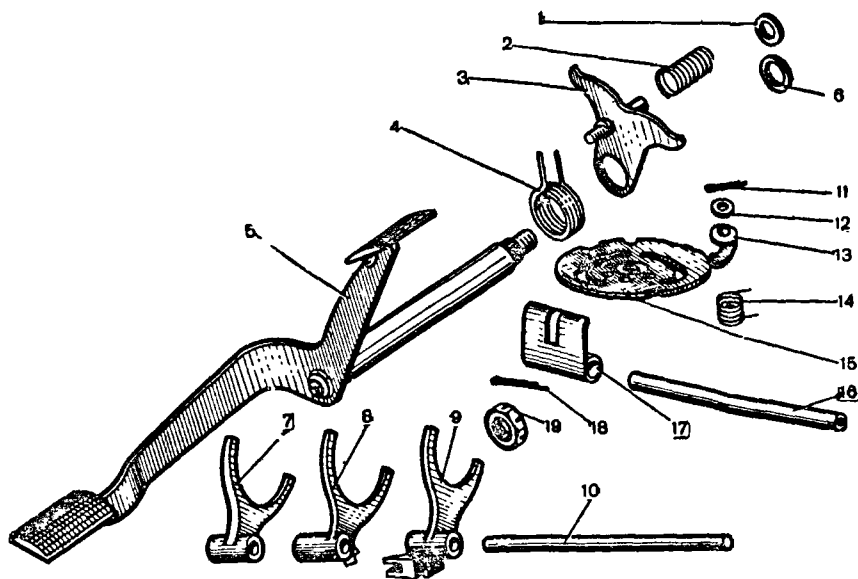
Детали механизма переключения коробки передач МТ-804:
